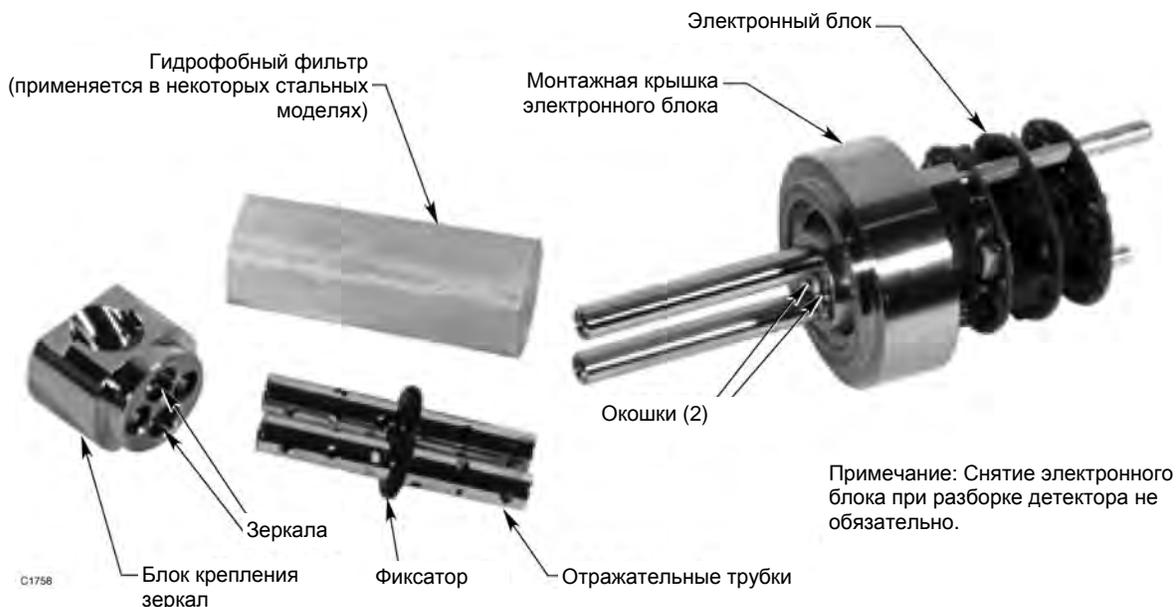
Разборка детектора в корпусе из нерж. стали для проведения чистки.
